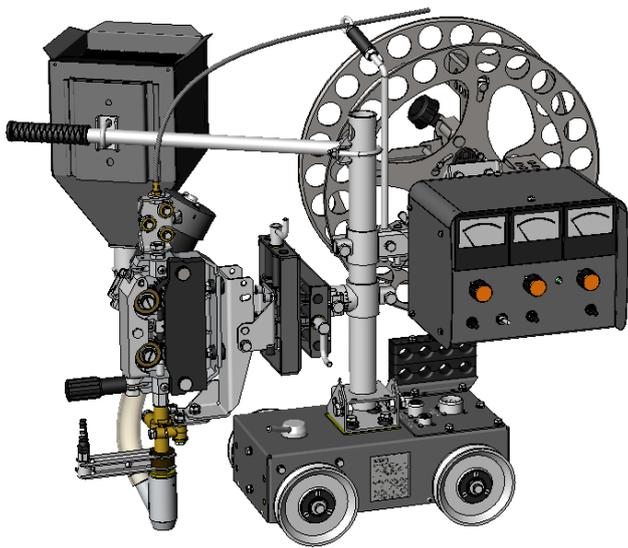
Автомат сварочный АДГ-630 исп.-03
